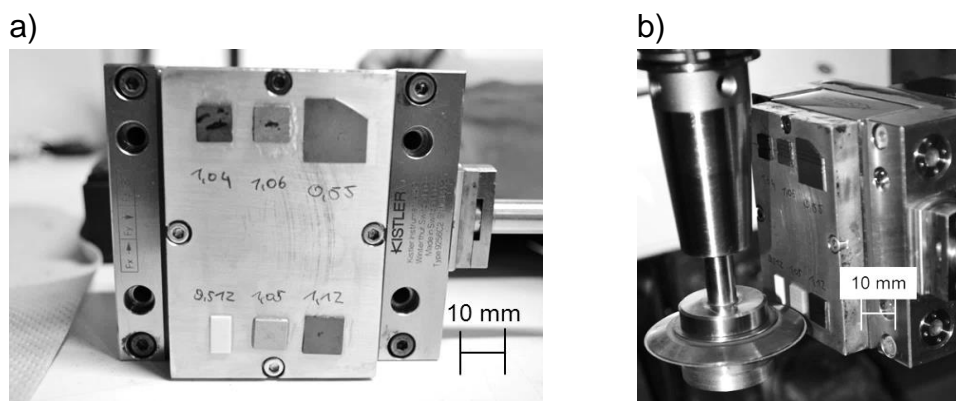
Werkstück a) und Werkzeug b) für Kraftmessungen
